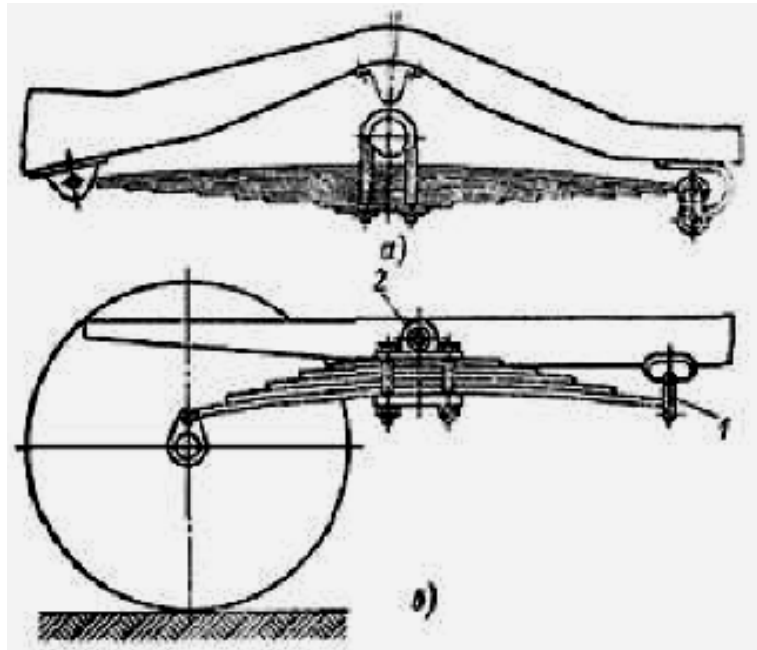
Рессорные зависимые подвески: а - с полуэллиптической рессорой; б - с кантилевой рессорой
